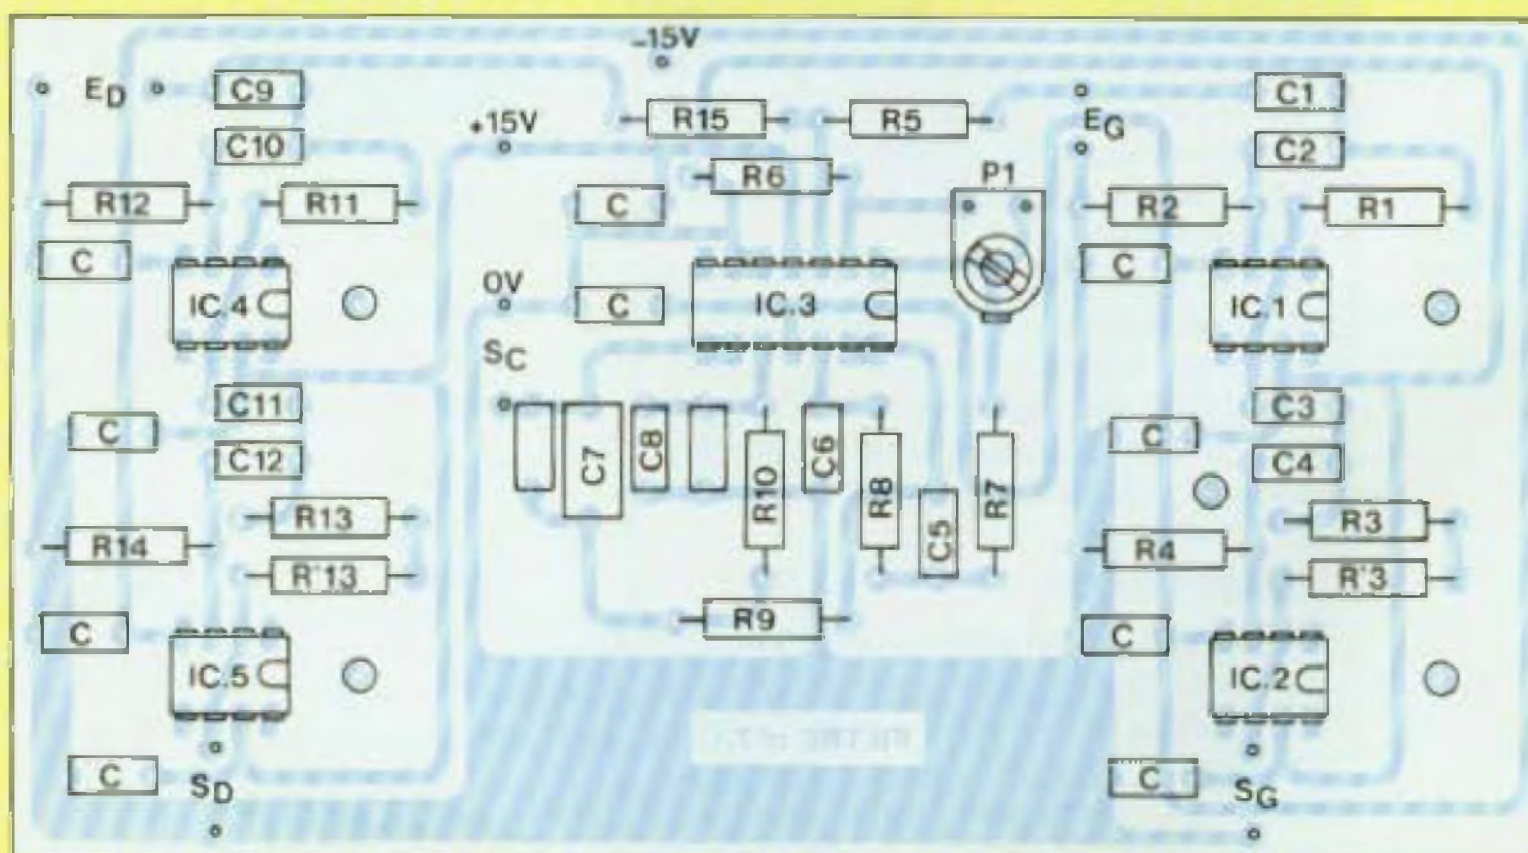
Le plan de câblage du filtre actif est suffisamment précis pour éviter toute erreur.
